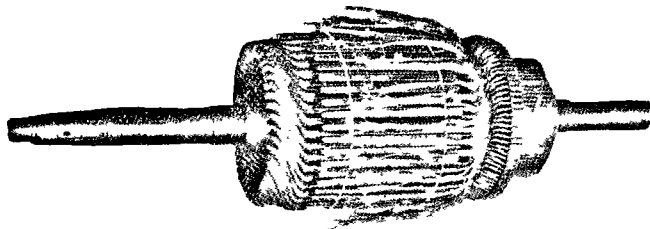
Armature avec sa première couche connectée au collecteur.
